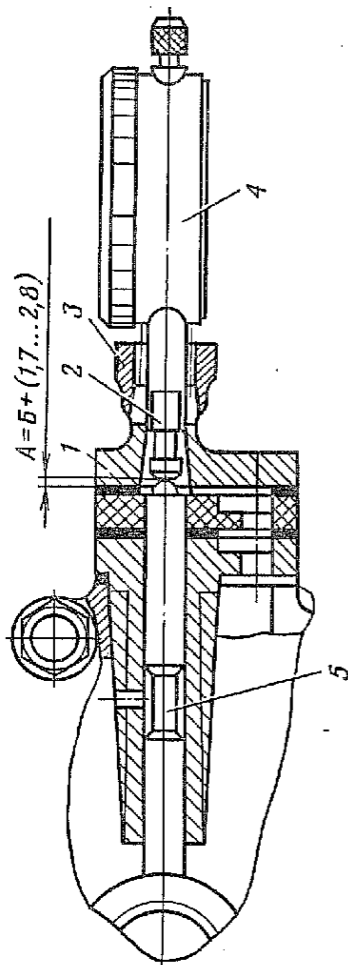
Приспособление для замера выступающей штанги привода топливного насоса:
